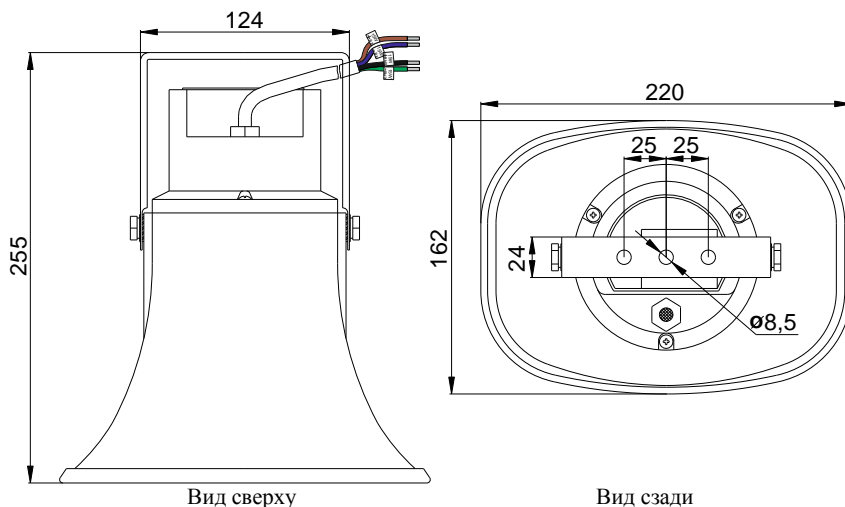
Внешний вид и габаритные размеры корпуса оповещателя
